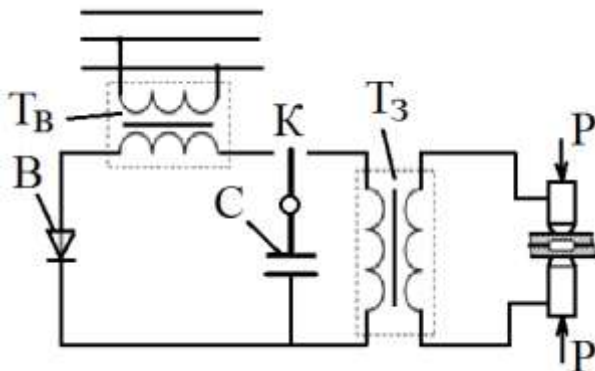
Схема точкового зварювання на конденсаторній машині
